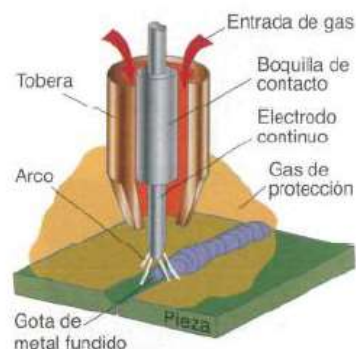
Proceso de soldadura MIG-MAG.
